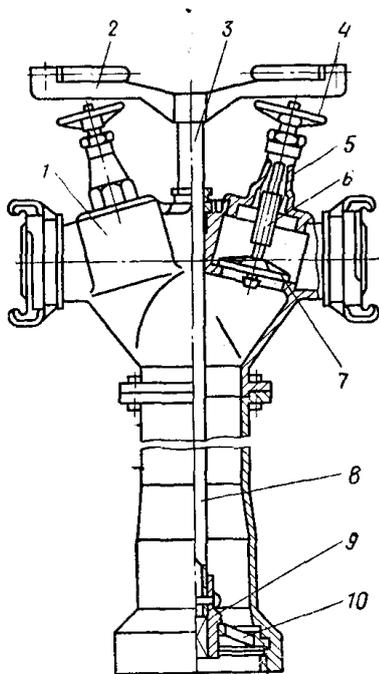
Пожарная колонка: 1 – головка; 2 – рукоятка; 3 – торцевой ключ; 4 – маховичок; 5 – крышка; 6 – шпindelь; 7 – тарельчатый клапан; 8 – корпус; 9 – квадратная муфта; 10 – бронзовое кольцо
